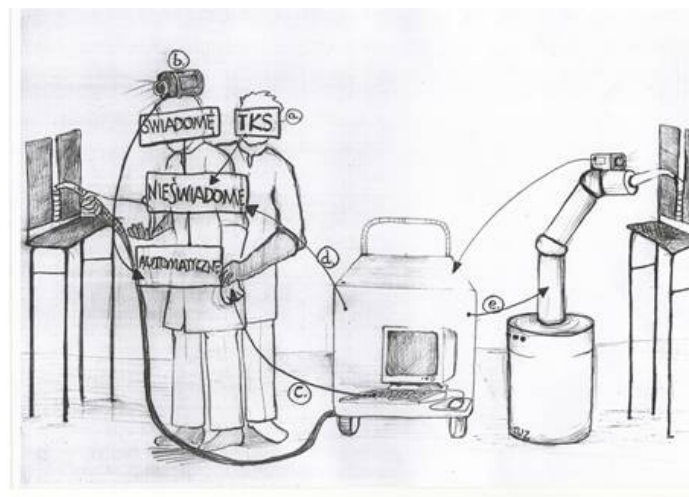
La idea de investigaciones sobre la inteligencia en la soldadura
